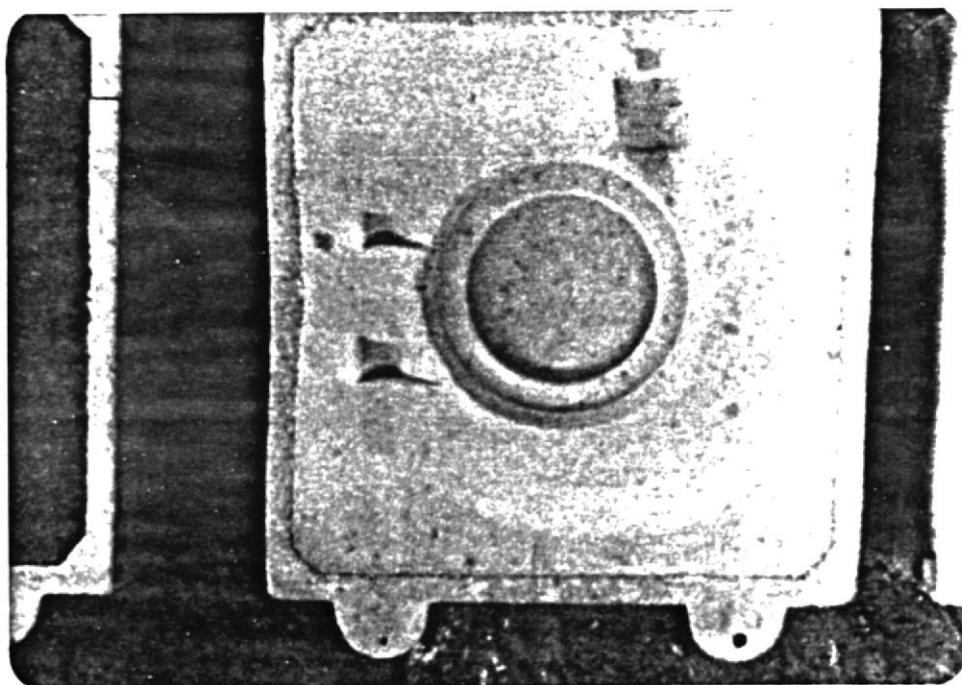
Fondo de un Molde de Bomba Centrífuga
